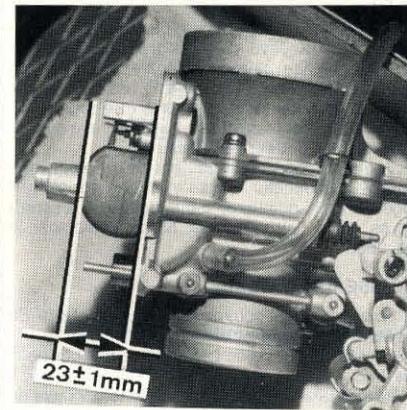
Hauteur correcte de flotteur (Photo RMT)
